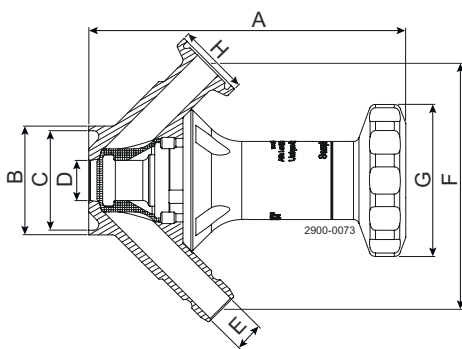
Handoberteil mit Ventilgehäuse: Rohr mit Kragen Schweißen
